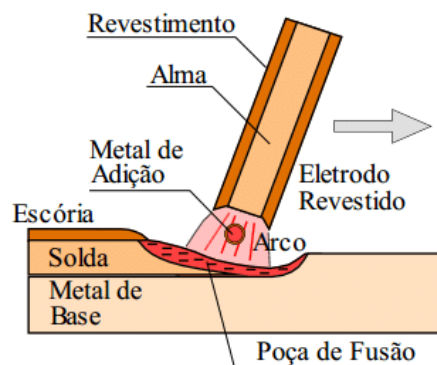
Representação de soldadura com eléttrodos revestidos.
